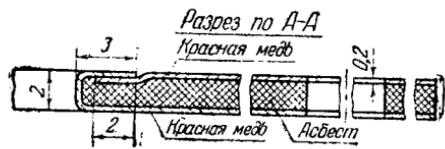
Дет. № 40268. Прокладка фланца всасывающей и выхлопной труб
